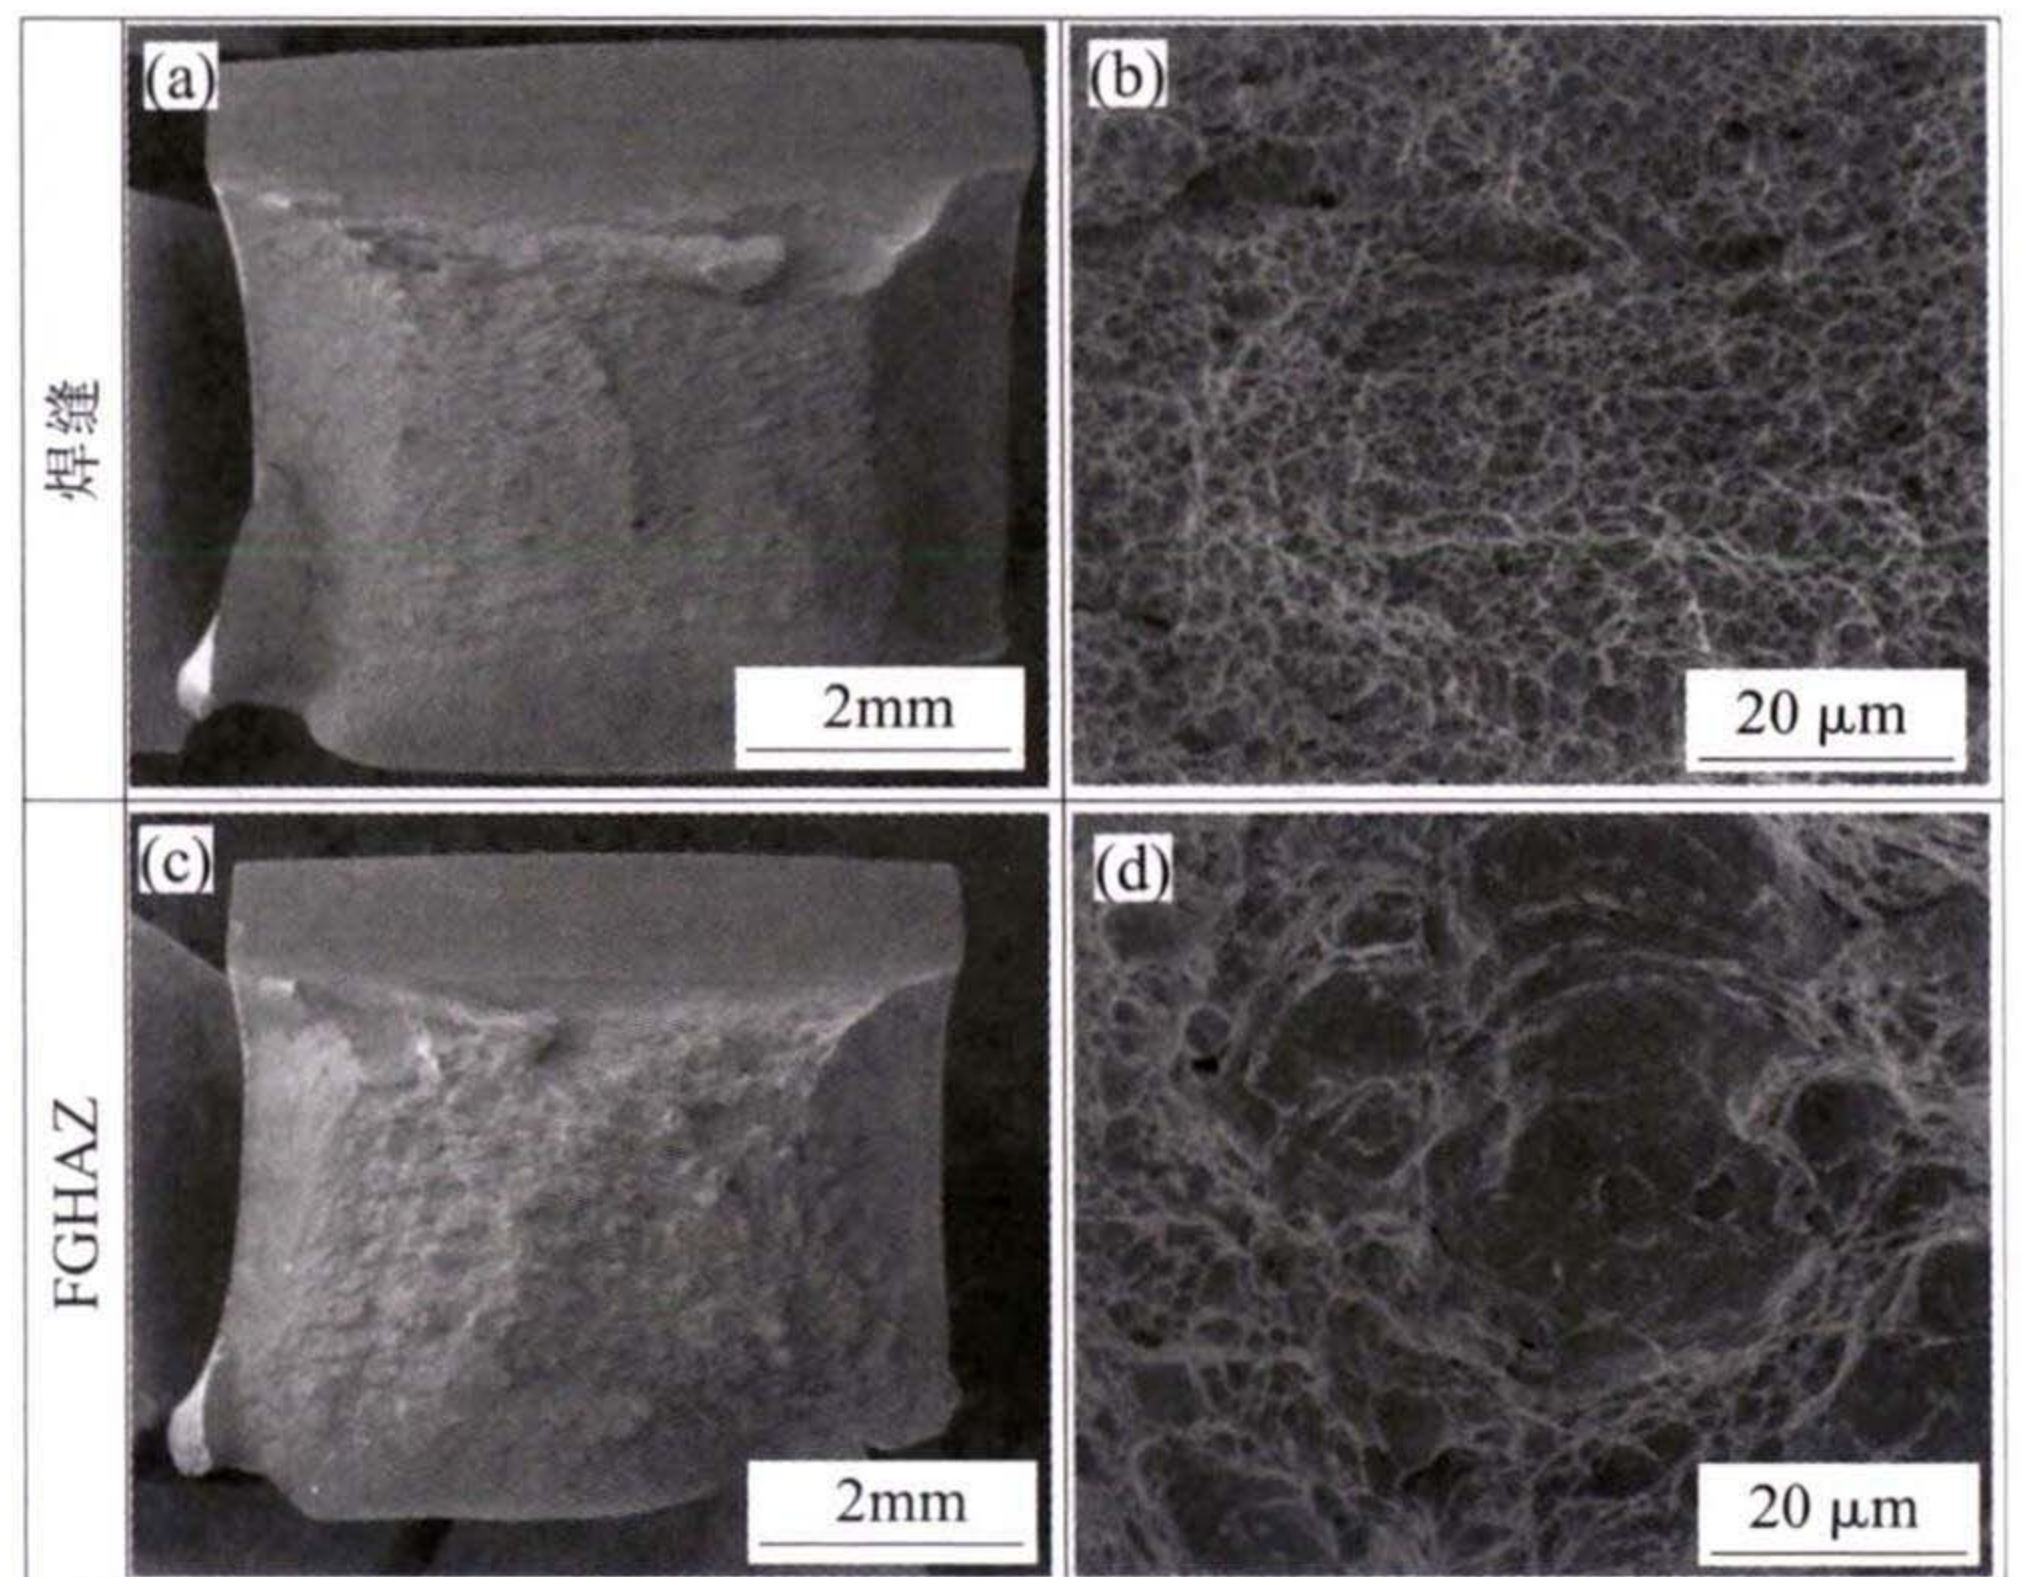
焊缝和细晶热影响区的冲击断口形貌
